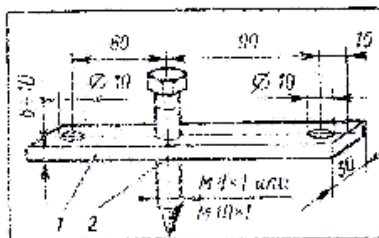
Приспособление для разборки и сборки сцепления тяжелых мотоциклов:
